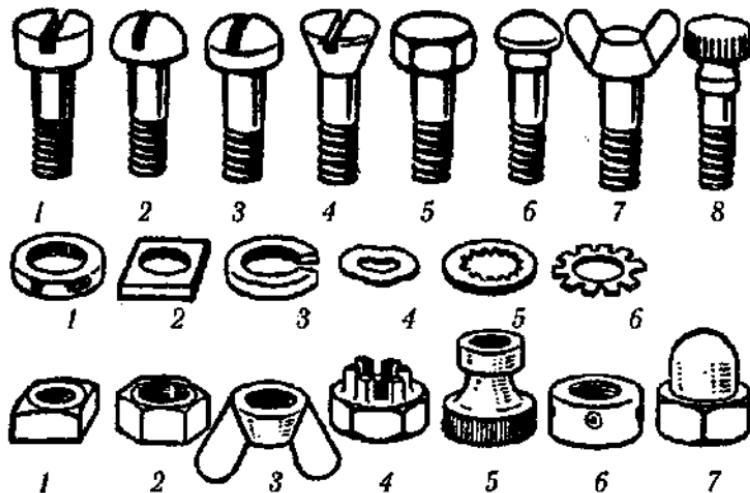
Крепежные детали. Винты: 1 — с цилиндрической головкой; 2 — с полукруглой головкой; 3 — с полупотайной головкой; 4 — с потайной головкой; 5 — с шестигранной головкой; 6 — с плосковыпуклой головкой; 7 — барабашковый; 8 — с накатанной головкой.
